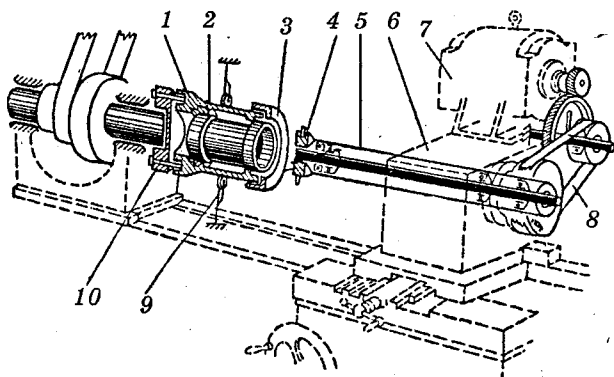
Приспособление к токарному станку для скоростной расточки гильз:
